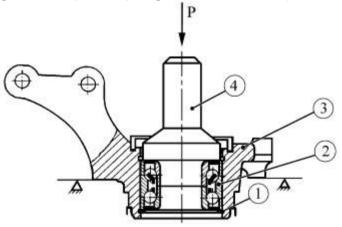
Выпрессовка из кулака и запрессовка в кулак подшипника ступицы переднего колеса:
